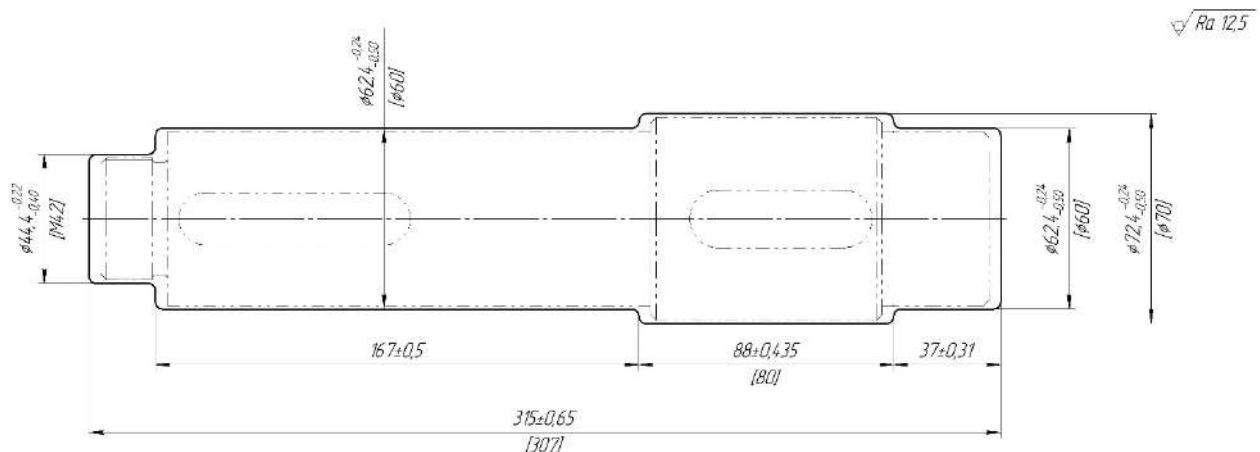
Ескіз заготовки, що отримана поперечно клинковою прокаткою
